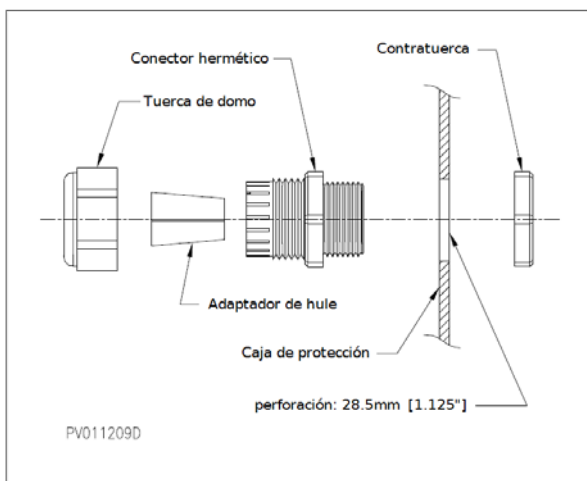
Montaje de los conectores de alivio de esfuerzo a prueba de agua para cable reforzado.
